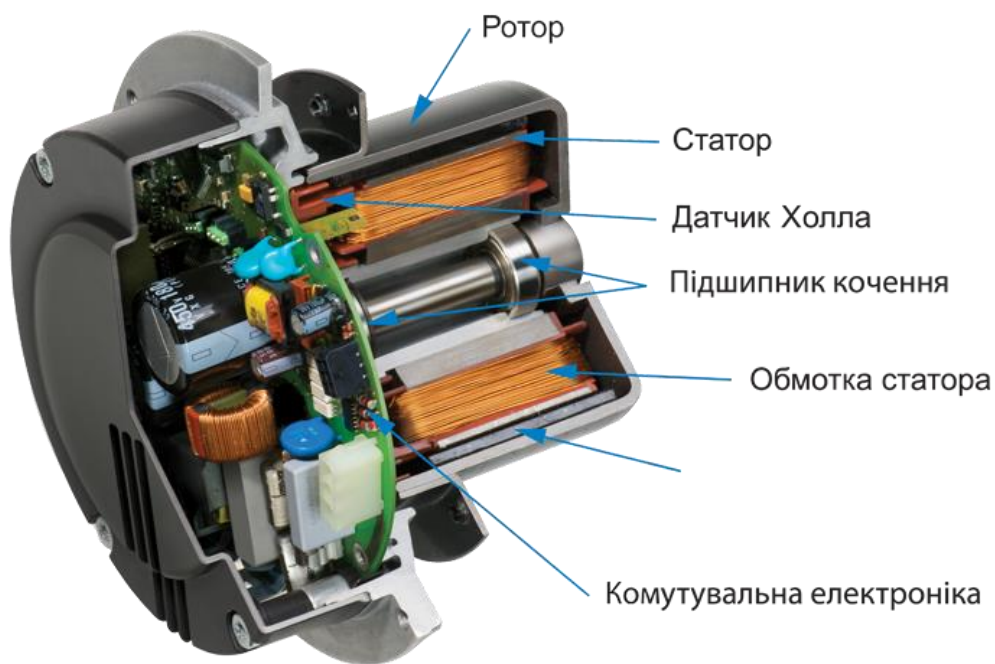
Будова вентильного двигуна з зовнішнім ротором
